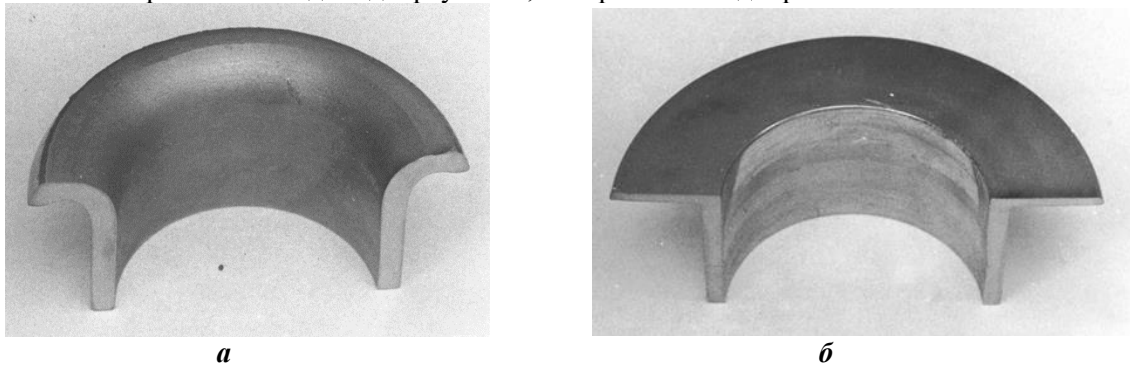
Вигляд трубної заготовки, отриманої за схемою відбортування методом ШО: а – проміжна стадія; б – заключна стадія
